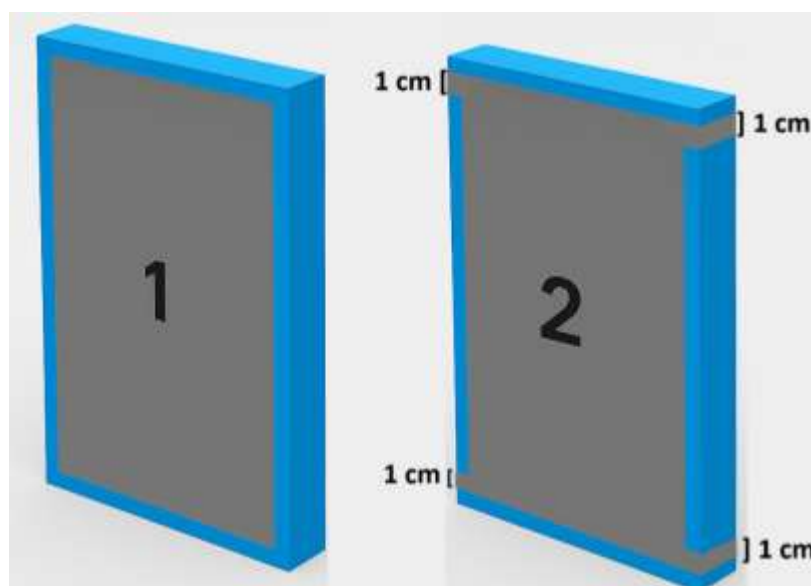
Soldadura perimetral total (izquierda) y parcial (derecha)
